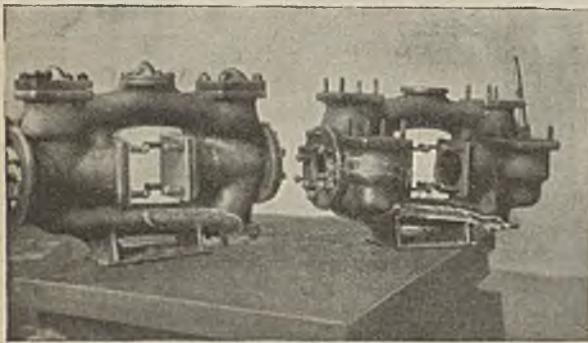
Geschweißtes Duplexpumpengehäuse.
